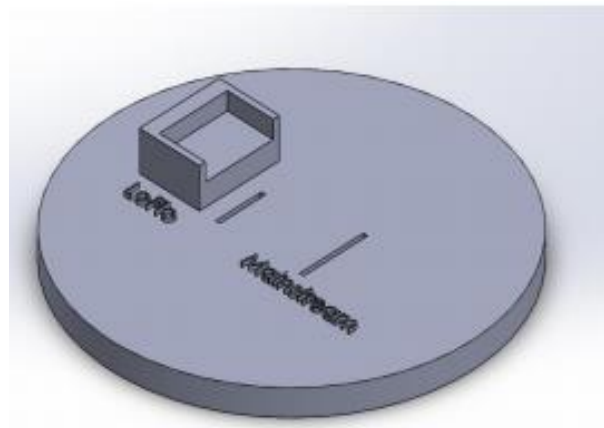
Fixture para operación de soldadura de L Flex, vista 1.
